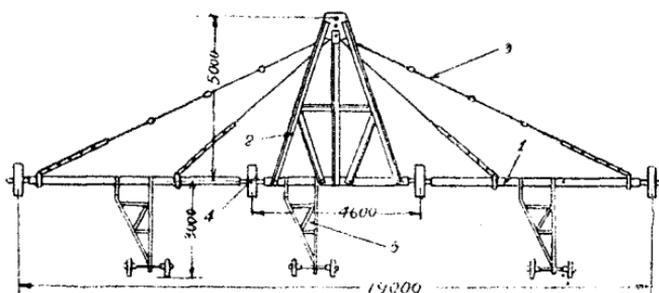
б. Общий вид сцепки С-18: 1—брусья, 2—сницы, 3—растяжки, 4—ходовые колеса, 5—удлинитель.
